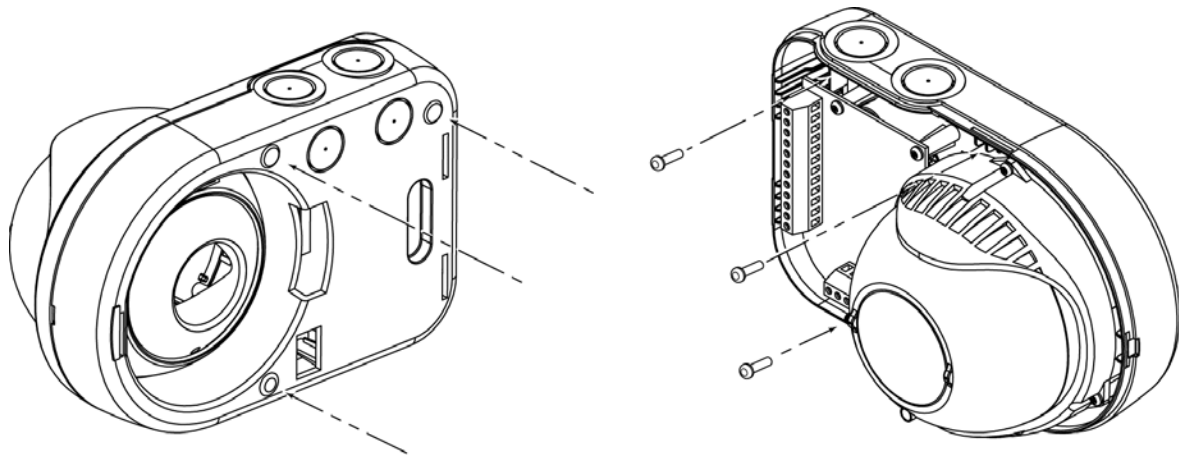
Montage direct de l'assemblage arrière de l'unité
